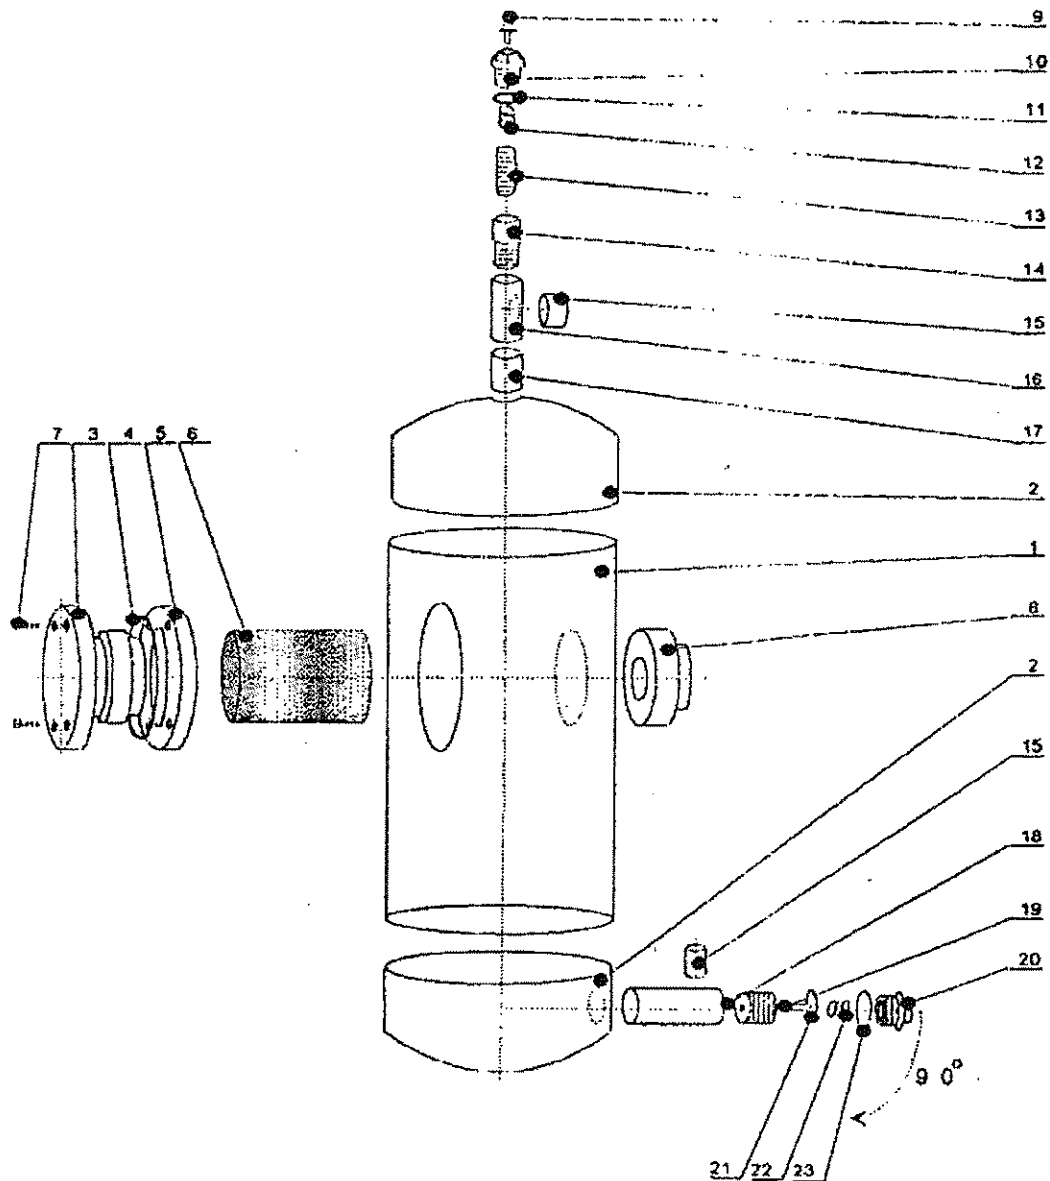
Rozmiestnenie komponentov v stojane typu 899.. /LPG
